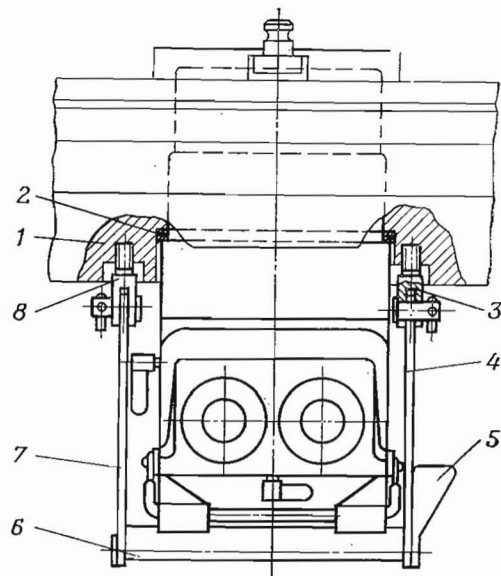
Установка прибора ТВНЕ-4Б по боевому:
